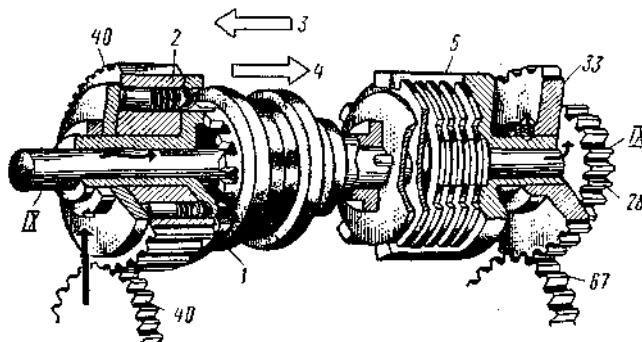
Муфти коробки подач універсально-фрезерного верстата 6М82:
